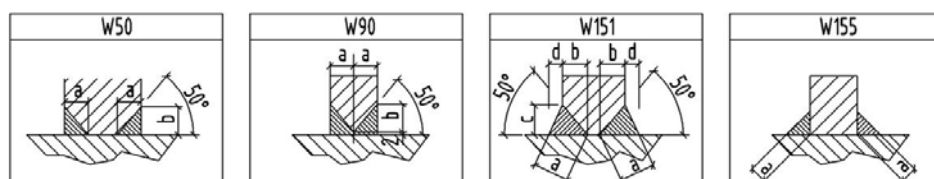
Schweißnahtausführungen (siehe Anlage F)
